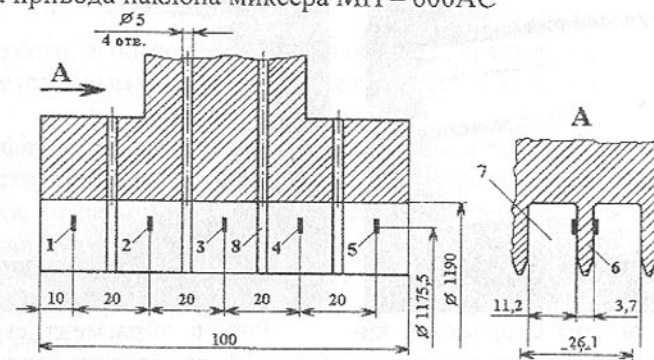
Схема расположения тензорезисторов на жестком колесе: 1, 2, 3, 4, 5 — тензорезисторы; 6 — контрольный зуб; 7 — сквозной продольный паз; 8 — радиальный разделительный паз
